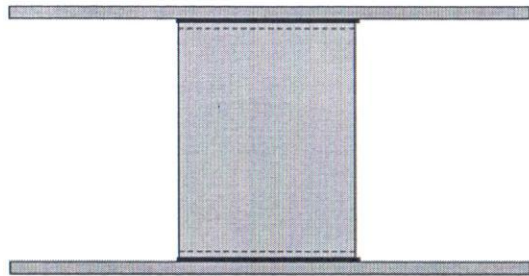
Контроль околошовных зон сварных соединений боковых планок затяжки с соединительной частью
